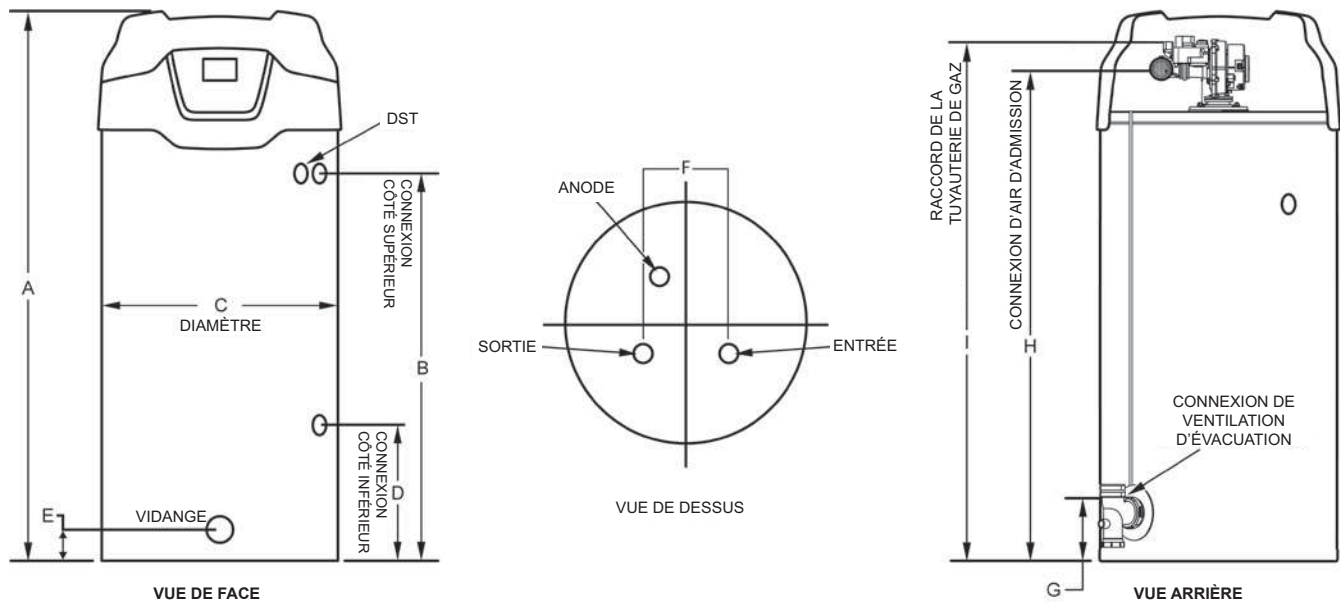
A : DIMENSIONS POUR UNITÉ 75 GALLONS
